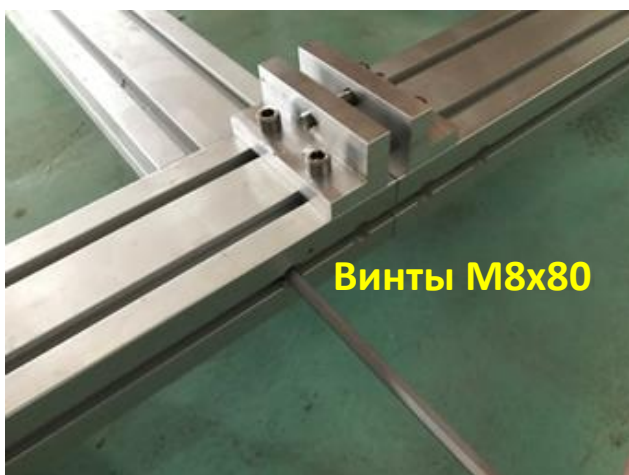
Установка нижней балки 6-ти метрового станка (2500x6000)
